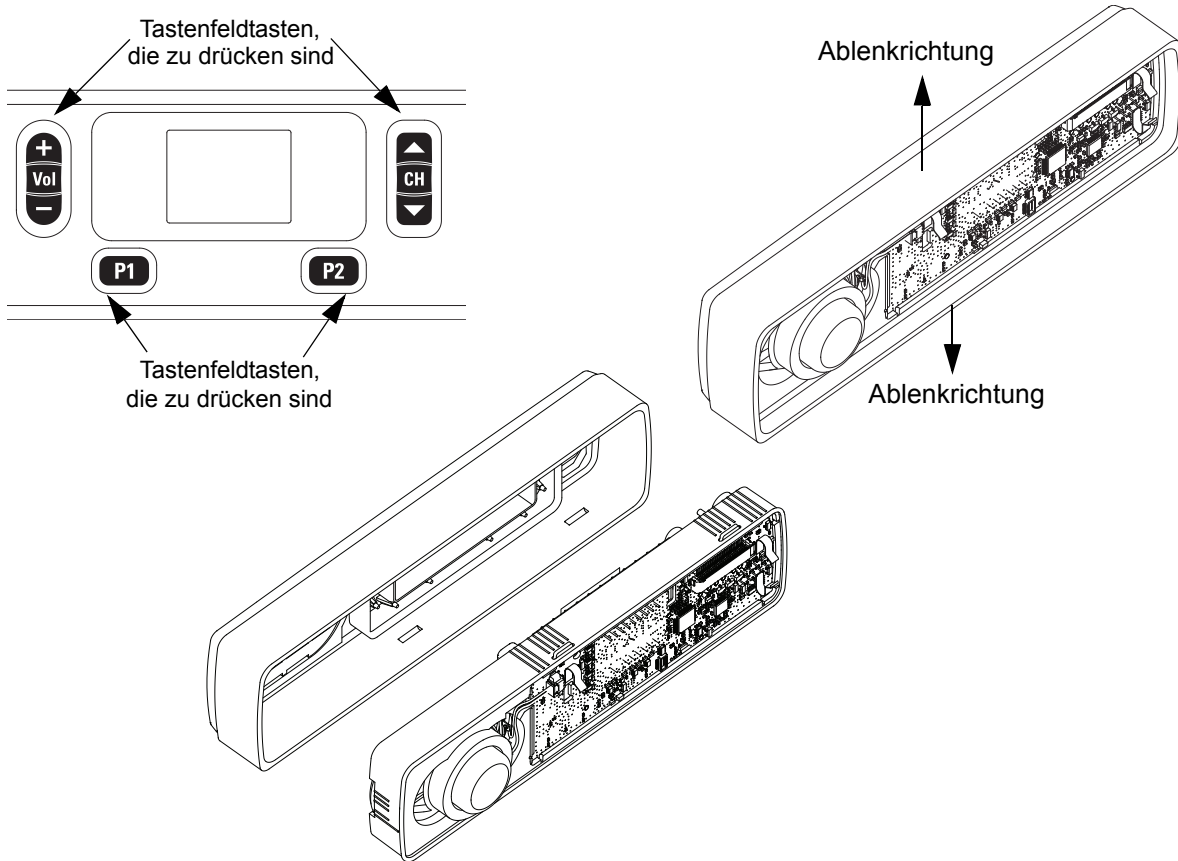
Tastenfeld-Baugruppe entfernen
